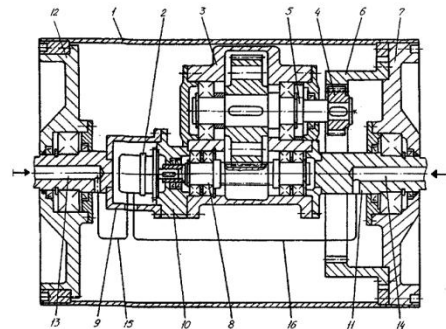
Гідравлічний приводний пристрій конструкції ВНТУ
